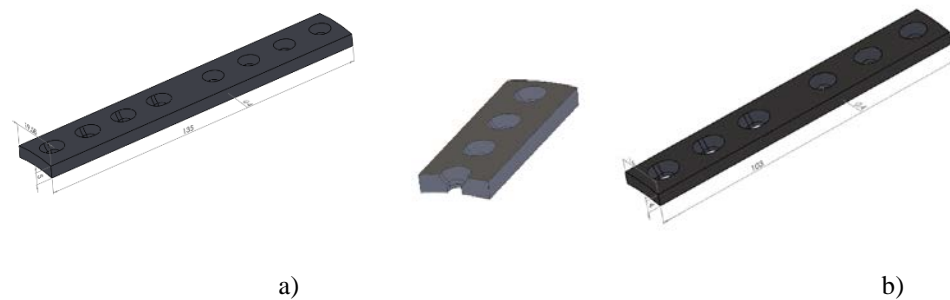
Modelo 3D das placas DCP (dimensões em mm): a) Placa de oito furos com pormenor do furo; b) Placa de seis furos.
